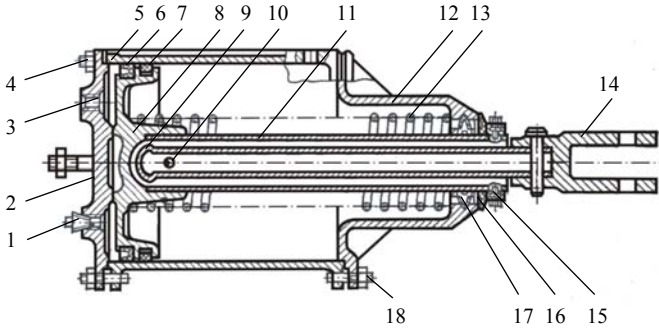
Тормозной цилиндр локомотивов с шарнирным соединением штока с поршнем
